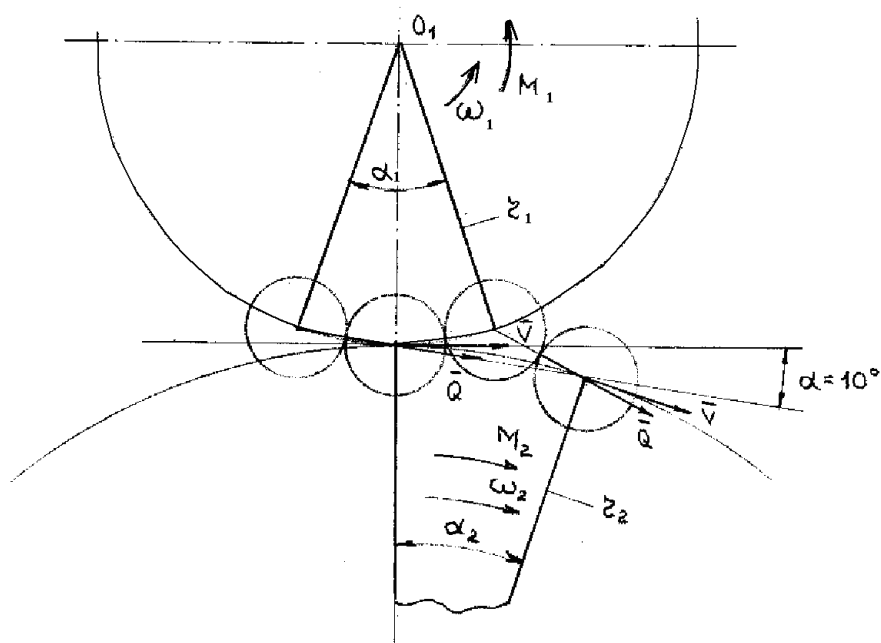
Двупарная передача с относительно подвижными цилиндрическими поверхностями зацепления (положение 2)
